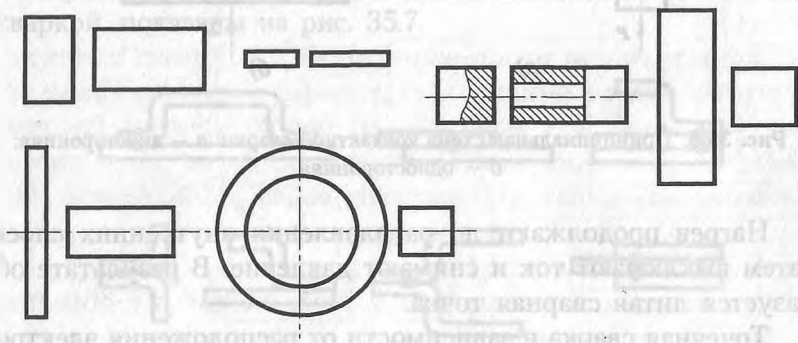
Примеры сварных соединений стыковой сваркой оплавлением
